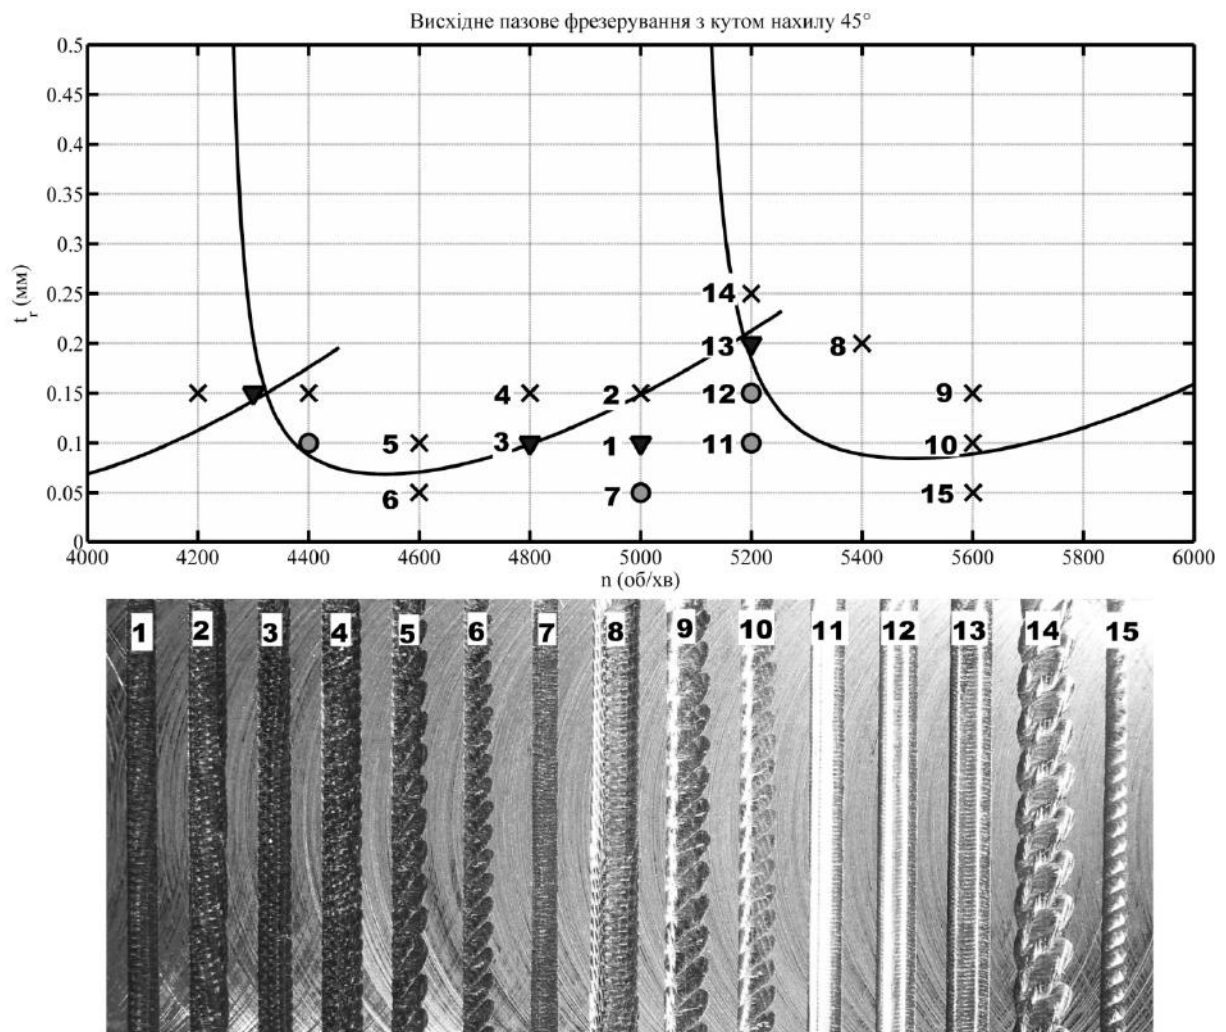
Результати проведених експериментів для обробки заготовки з поверхнею, нахиленою під кутом  $\varphi_a = 45^\circ$
